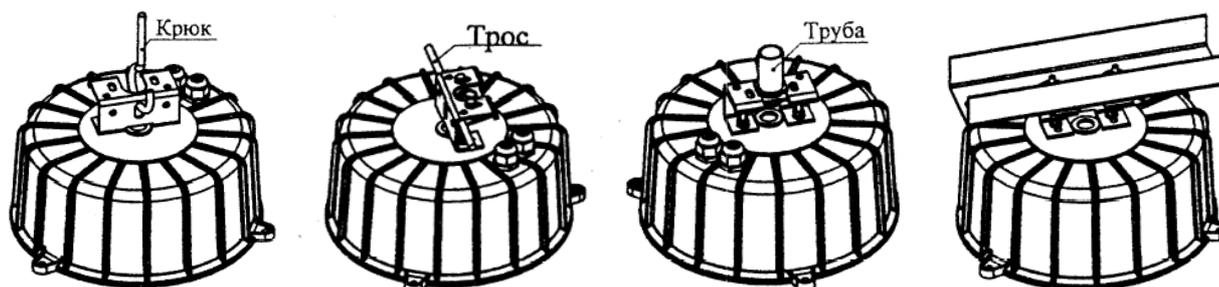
Универсальный узел крепления светильников GALAD Гермес ГСП/ЖСП51.
